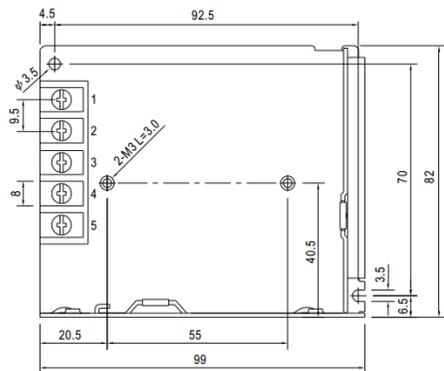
Габаритные размеры блоков питания LRS-35; LRS-50; LRS-60
